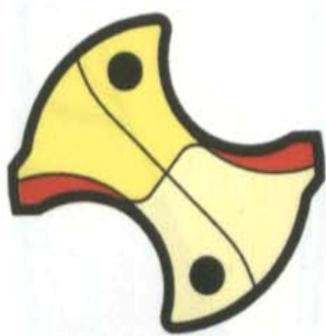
Desgaste de flanco (VB) ⁽¹¹⁾
